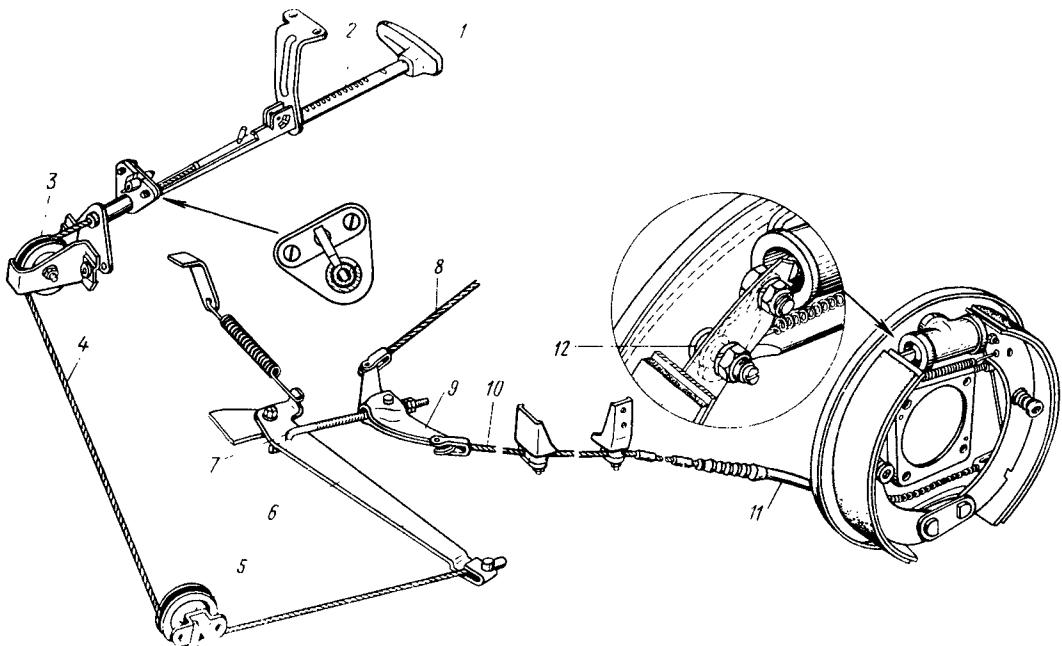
Стояночный тормоз, действующий на задние колеса:
